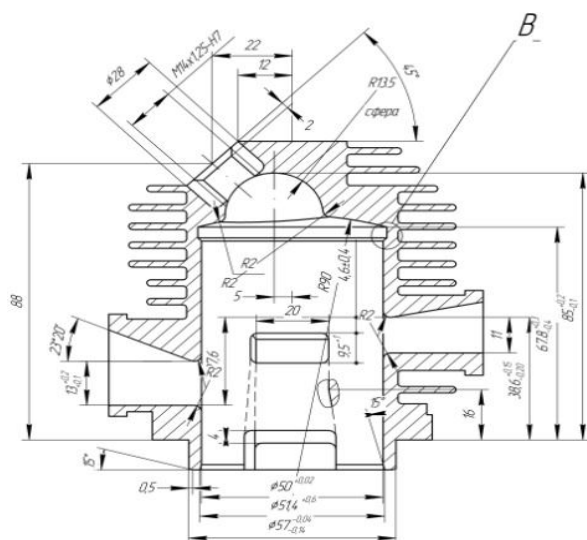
Корпусная деталь – цилиндр двухтактного двигателя
